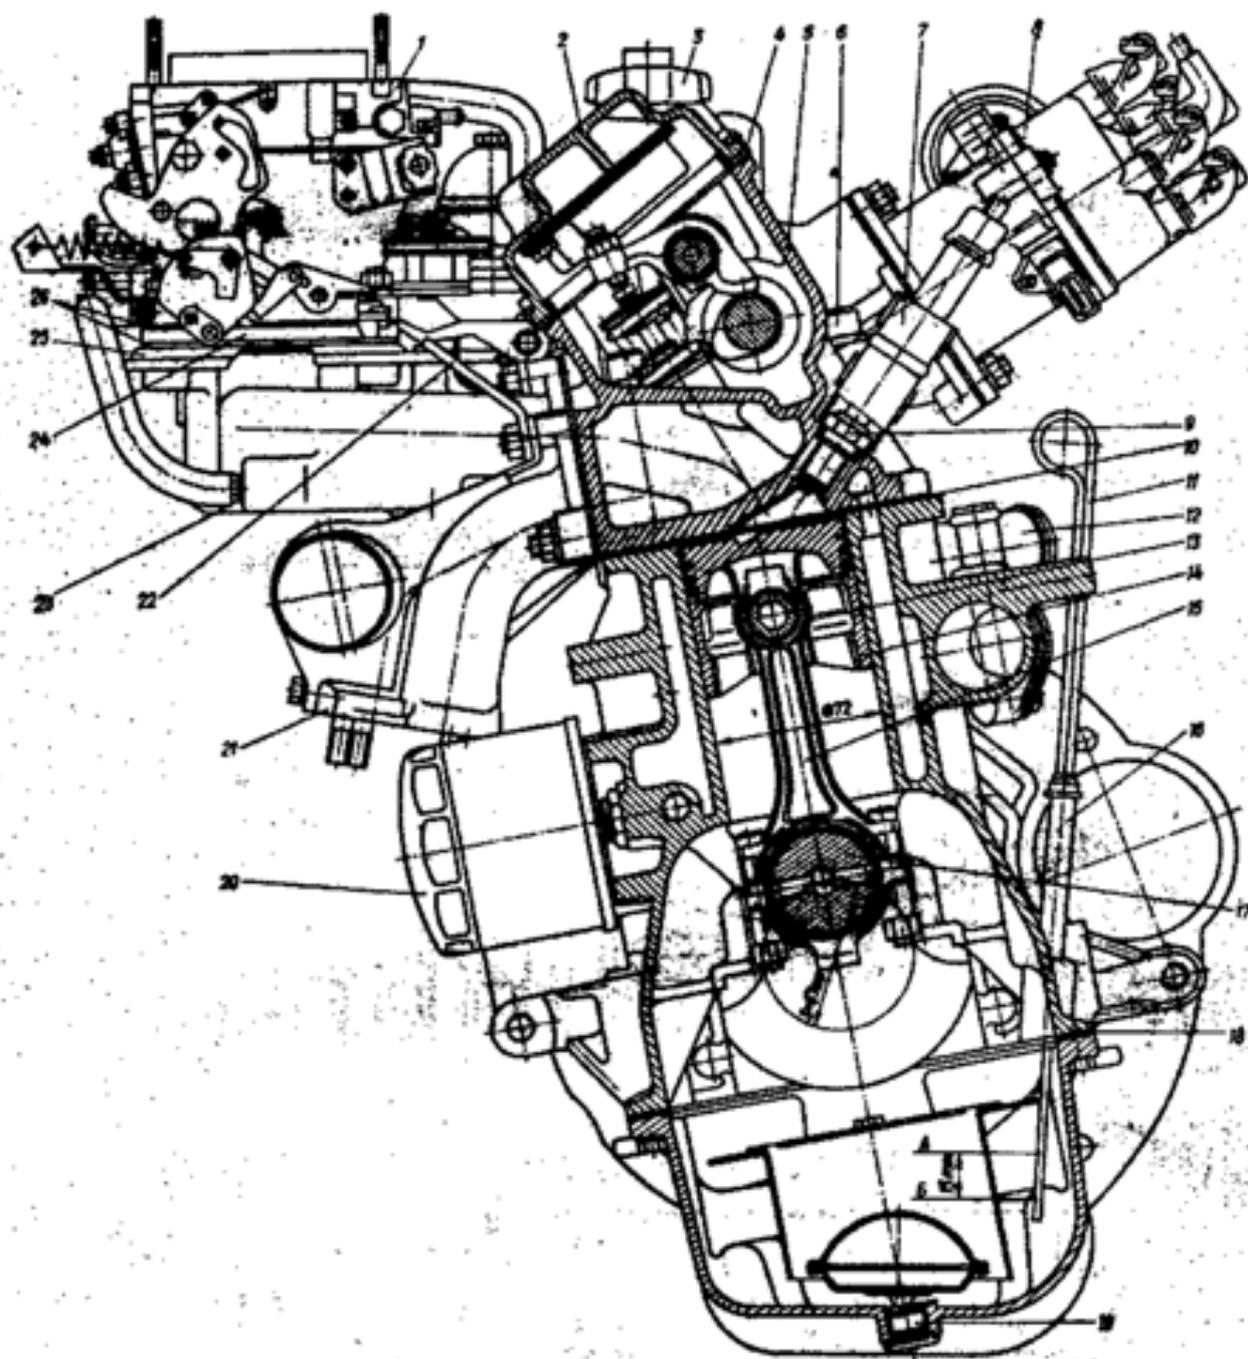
Поперечный разрез двигателя: 1-карбюратор; 2-крышка головки цилиндров; 3-крышка маслозаливной горловины; 4-прокладка крышки головки цилиндров; 5-головка цилиндров; 6-болт крепления головки цилиндров; 7-наконечник свечи; 8-датчик-распределитель; 9-свеча зажигания; 10-прокладка головки цилиндров; 11-маслоизмерительный стержень; 12-трубка, подводящая жидкость; 13-палец поршня; 14-поршень; 15-шатун; 16-трубка маслоизмерительного стержня; 17-коленчатый вал; 18-прокладка масляного картера; 19-маслозаливная пробка; 20-масляный фильтр; 21-выпускной коллектор; 22-рым-планка; 23-впускной коллектор; 24-проставка фланца; 25-топливосборник; 26-прокладка фланца карбюратора. Уровни масла: А-верхний, равный 3,45 л и Б-нижний, равный 2,45 л
